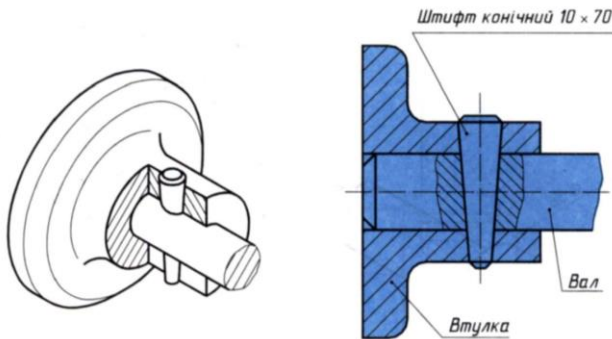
З'єднання деталей за допомогою конічного штифта
